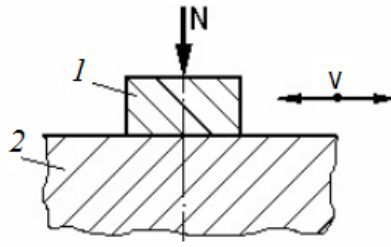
Розрахункова схема плоскої прямої зворотно – поступального руху: 1 – повзун (каретка супорта), 2 – основа (станина)
